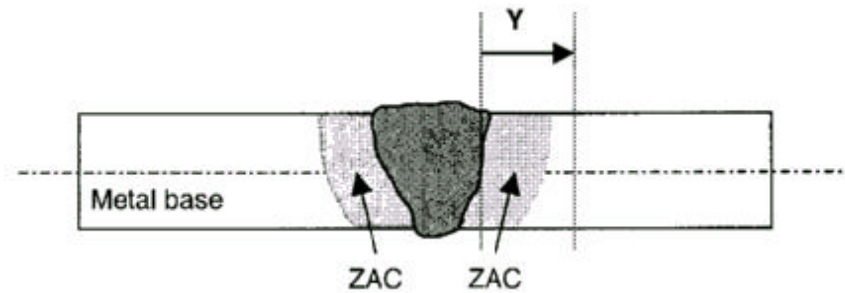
SOLDADURA CON PENETRACIÓN COMPLETA Y DE UNA SOLA PASADA
